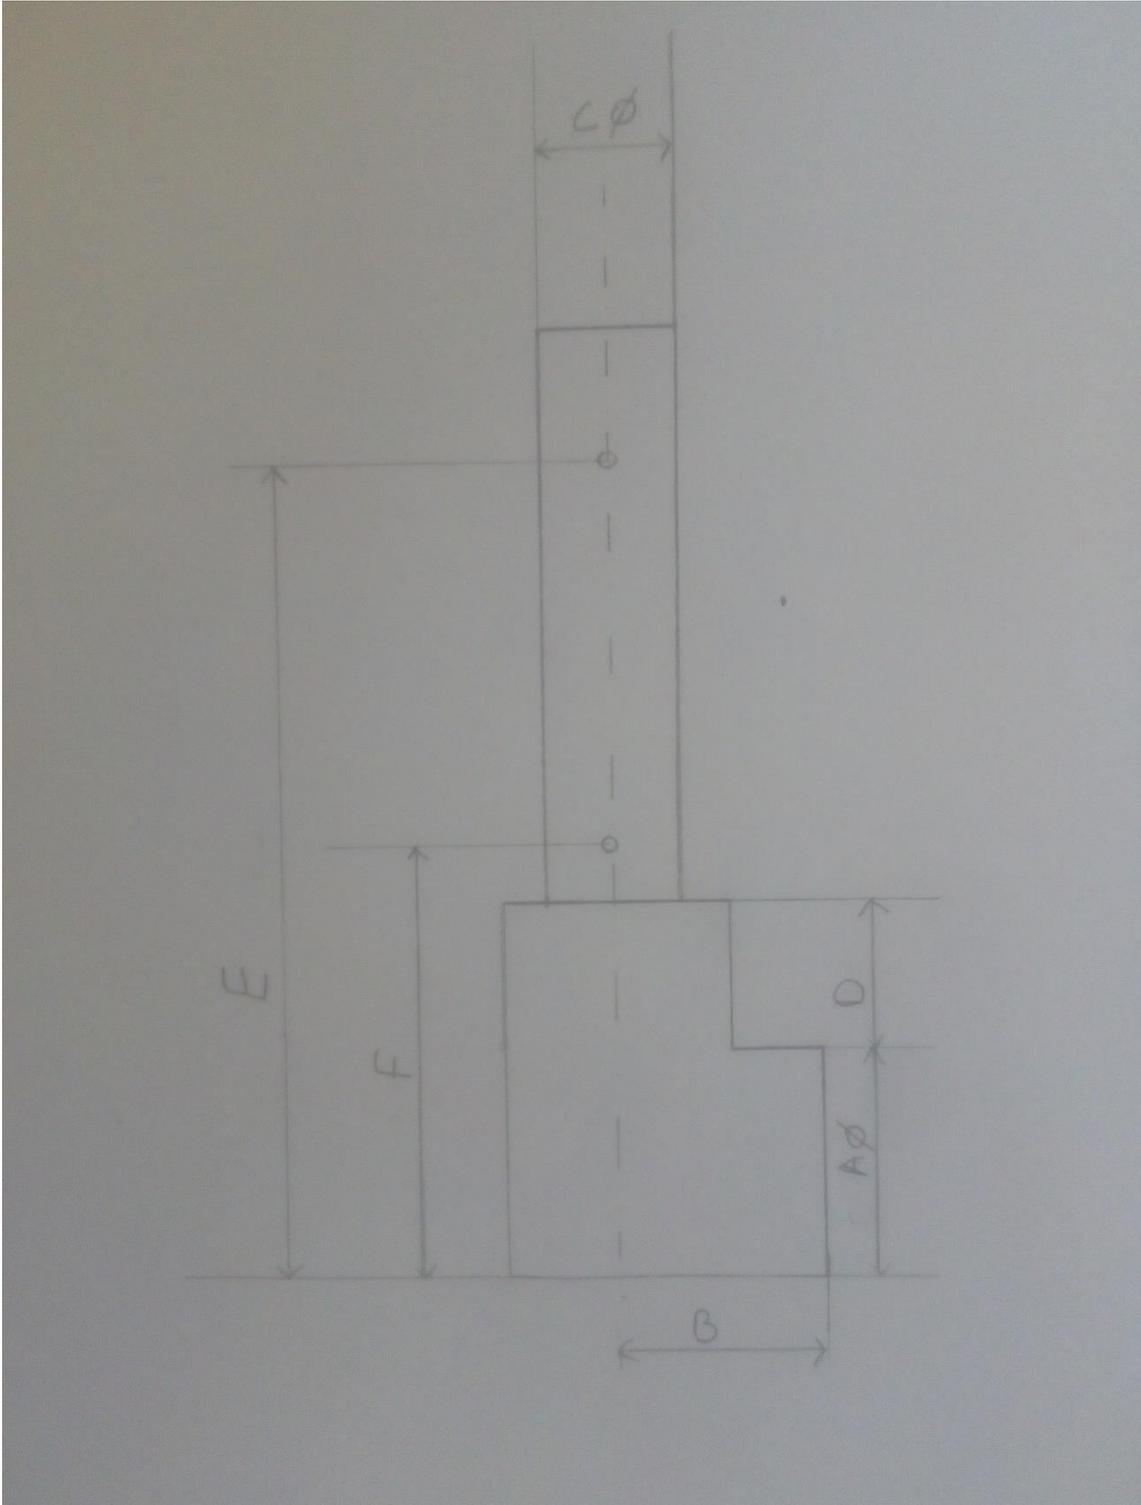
En la figura anterior se muestra un croquis del eje en L con las diferentes dimensiones que se habrán de definir.
